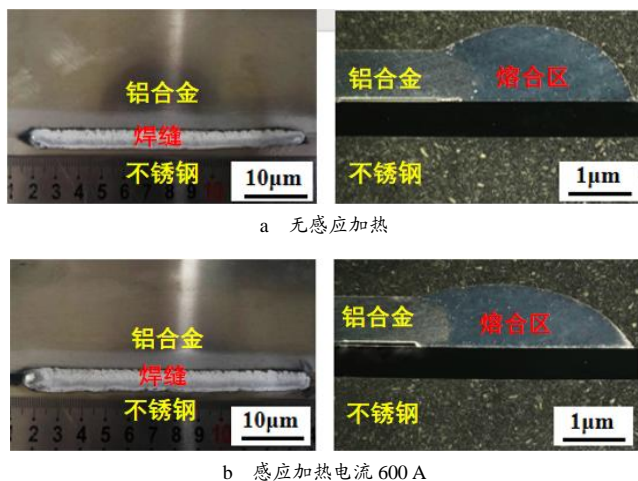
铝/钢接头焊缝成形及截面形貌
